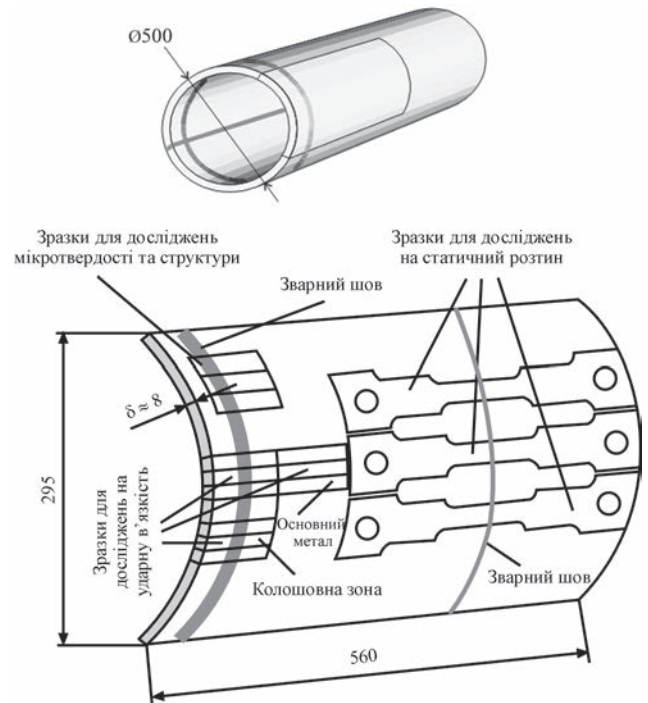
Схема виготовлення зразків з фрагменту контрольованої труби
